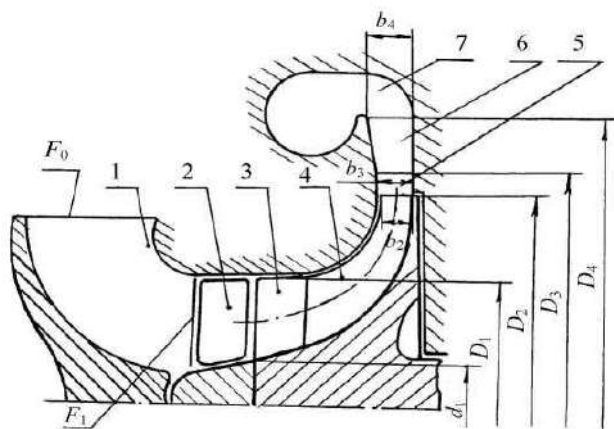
Схема проточної частини відцентрового компресора [5]:
